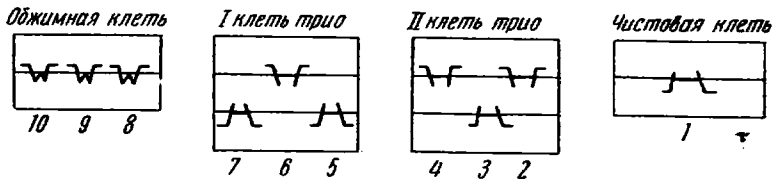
Схема прокатки балки № 30 (цифрами обозначены номера калибров)
